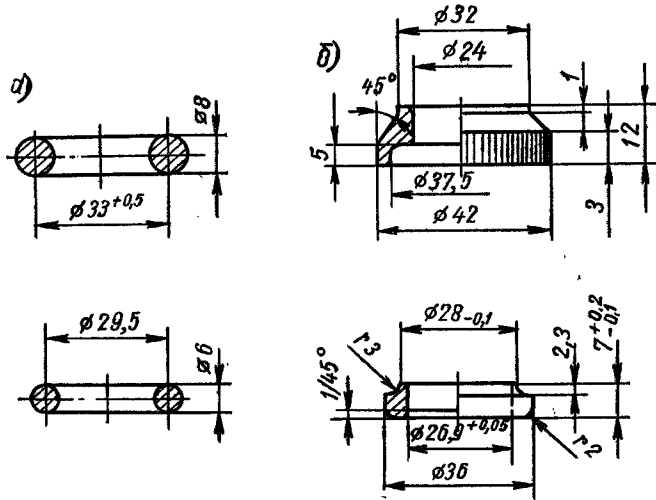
Стальные детали, полученные холодным выдавливанием из сварных кольцевых заготовок
